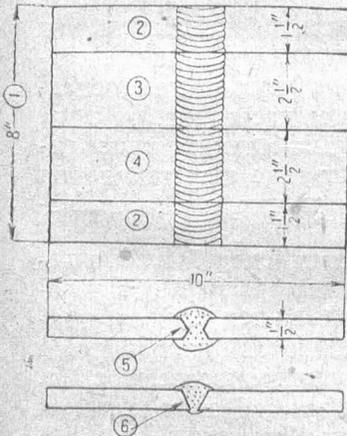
Сварные планки для изготовления образцов на разрыв и изгиб. 1 — при испытании на ударную вязкость длина планки должна быть не менее 265 мм; 2 — отбрасывается; 3 — образец для испытания на разрыв; 4 — образец для испытания на изгиб; 5 — двусторонний скос; 6 — односторонний скос
